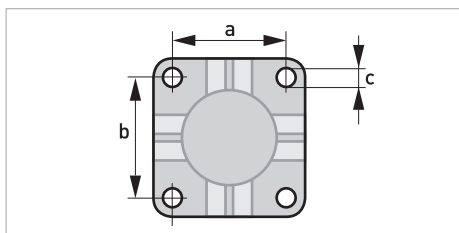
Dimensiones para placa de montaje del alojamiento de campo
